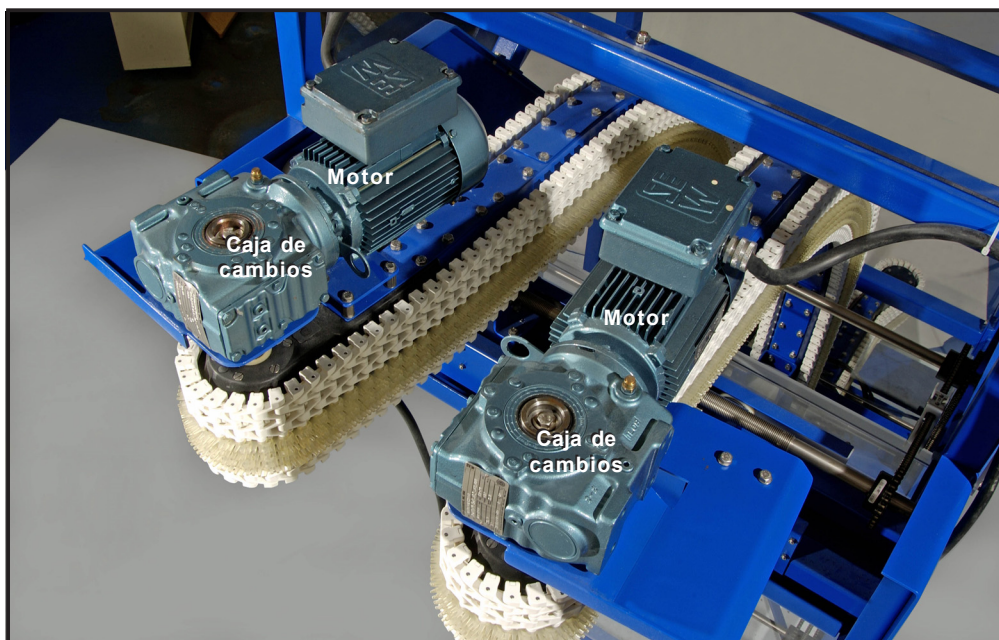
Motores con engranaje reductor del eje hueco, montado en ejes motores verticales (transportador de cuña)
